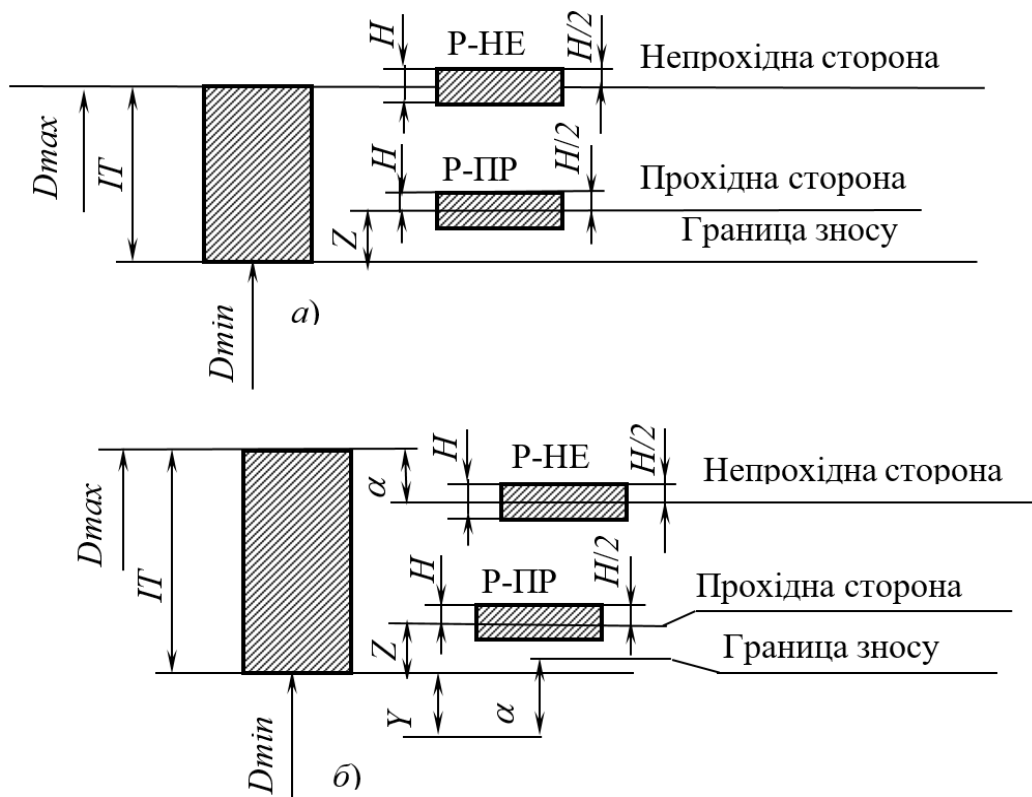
Схема розташування полів допусків калібрів:
